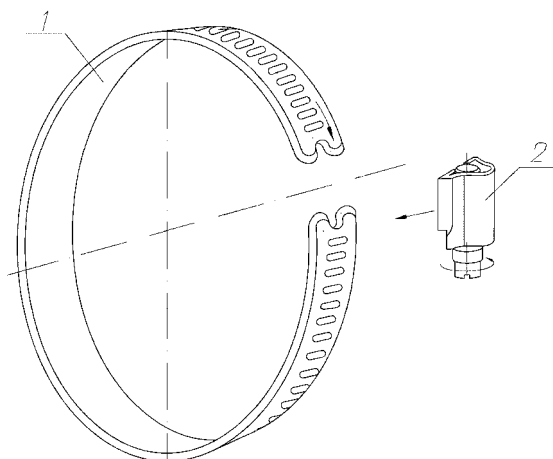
КМЧ для ППТП с корпусом типа «К1»
